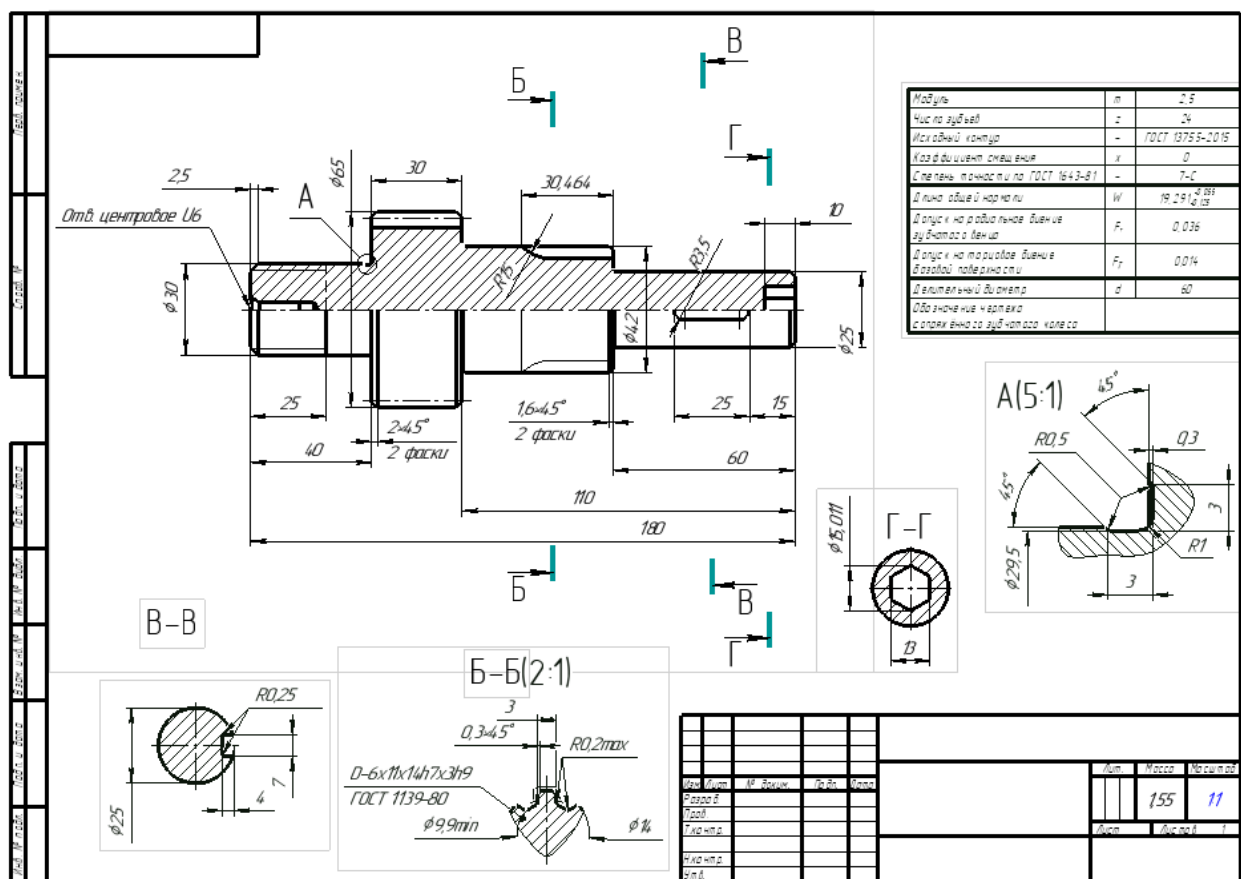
Чертеж вала-шестерни созданного в приложении «Валы и механические передачи 2D»
